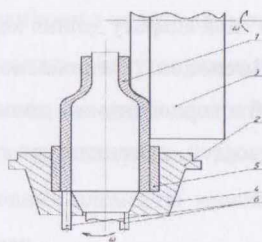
Схема формування горловини трубної заготовки; 1 заготовки, 2 матриця, 3 валок циліндричний, 4 оправка, 5 втулка, штовхачі 6.
